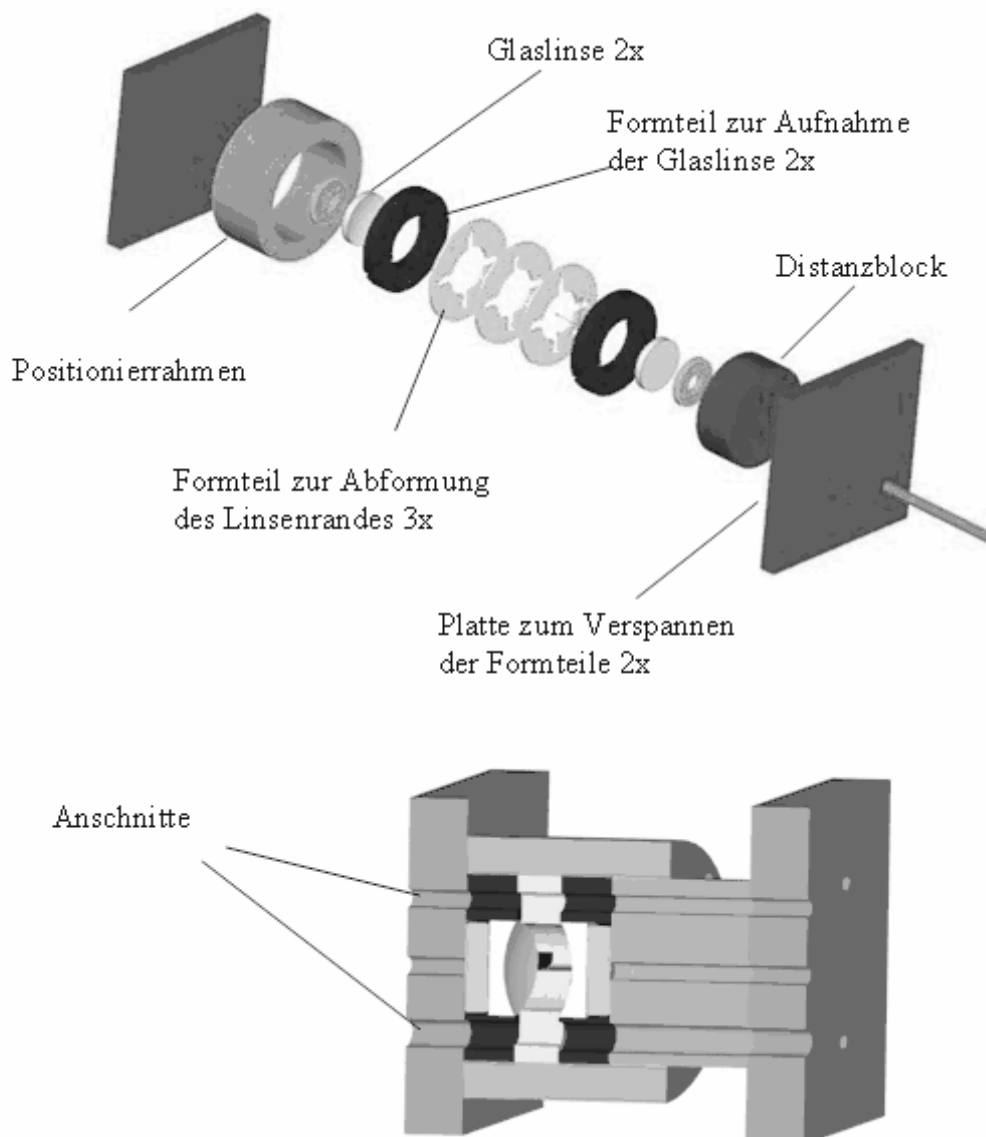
Oben: Explosionsansicht des Abformwerkzeuges der elastischen Linse. Unten: Zusammenbau der Form.
